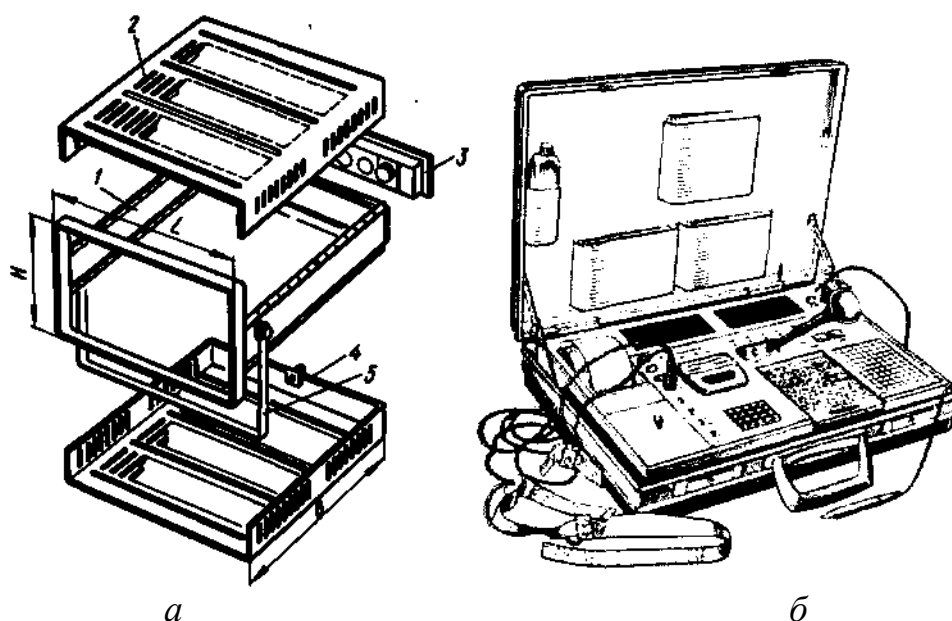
Конструкция унифицированного корпуса настольного переносного измерительного прибора (*а*): 1 — каркас; 2 — верхняя крышка; 3 — задняя стенка; 4 — нижняя крышка; 5 — откидная ручка-подставка и общий вид переносного портативного комплекса (*б*)
